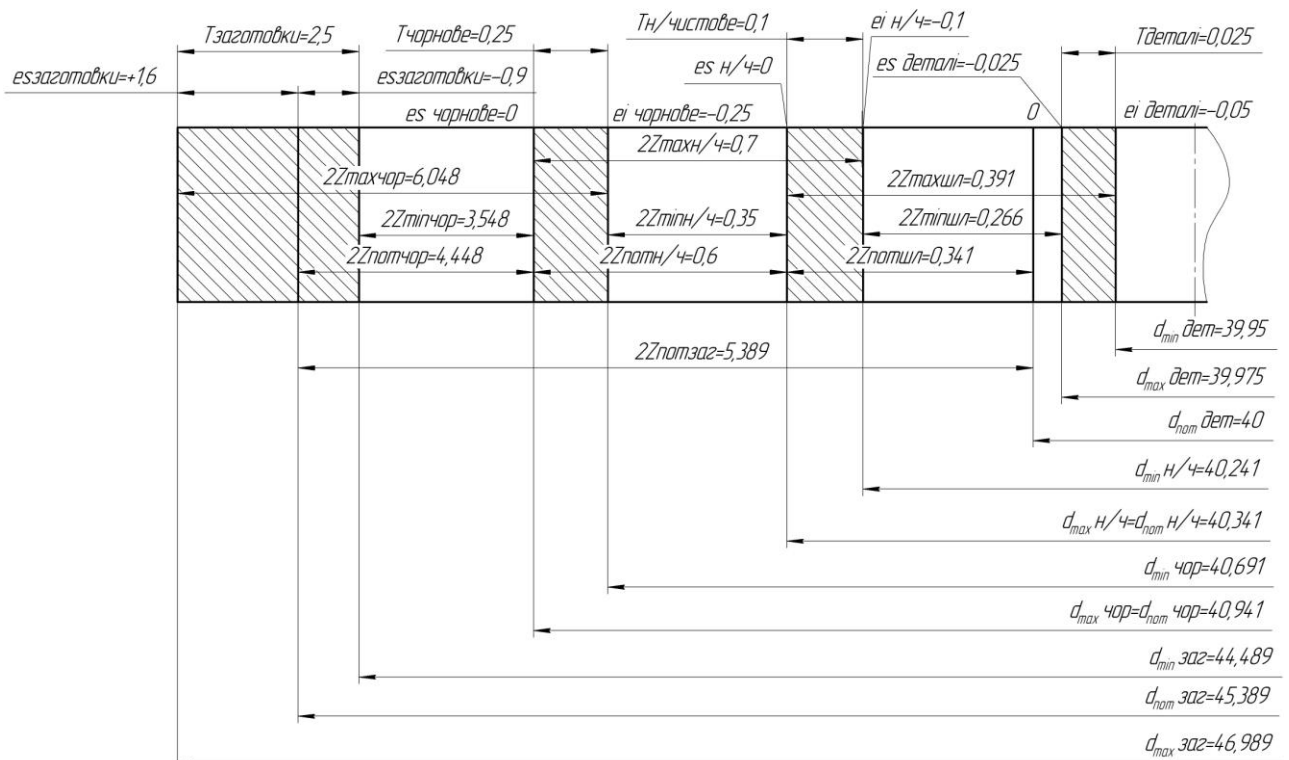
Схема розташування припусків і допусків для поверхні  $\varnothing 40f7$ .
